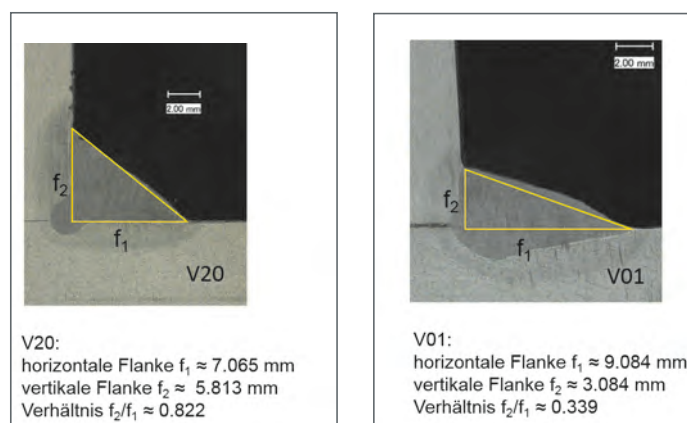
Schweißnähte und Nahtflankenverhältnis bei verschiedenen Schweißbrennerpositionen
